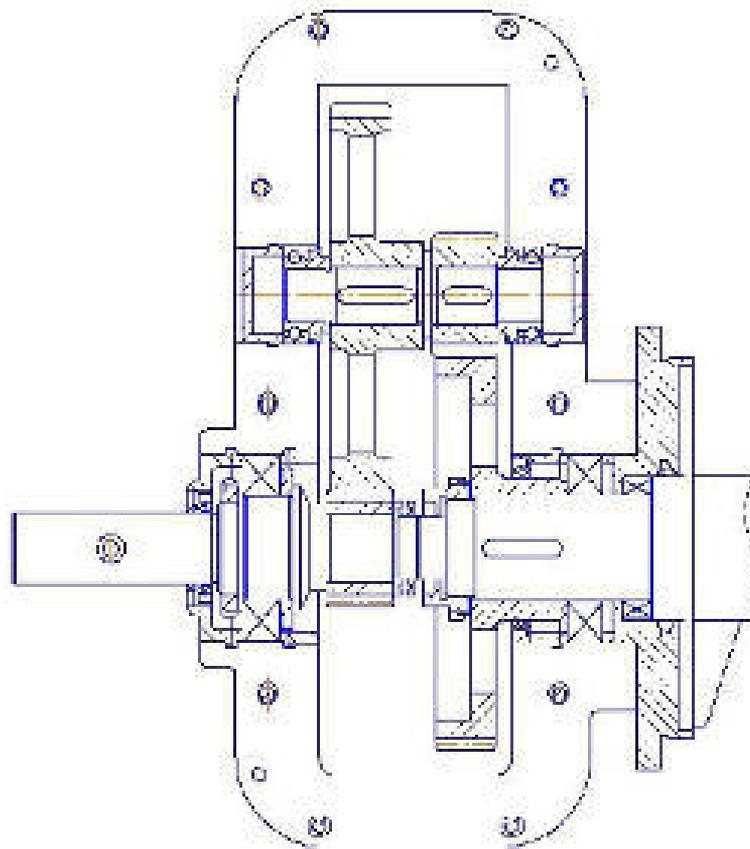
Двухступенчатый цилиндрический редуктор с двумя рабочими валами, расположенными коаксиально
